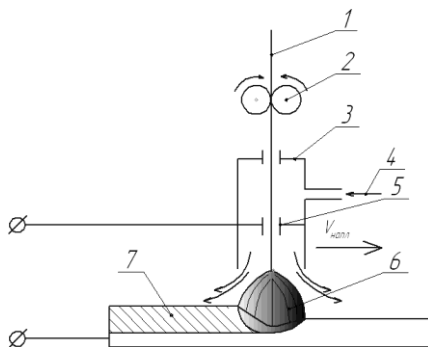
Схема наплавлення покриття: 1 – зварювальний дріт; 2 – подаючі ролики; 3 – сопло; 4 – захисний газ; 5 – струмопідвід; 6 – дуга; 7 – наплавлений валик
